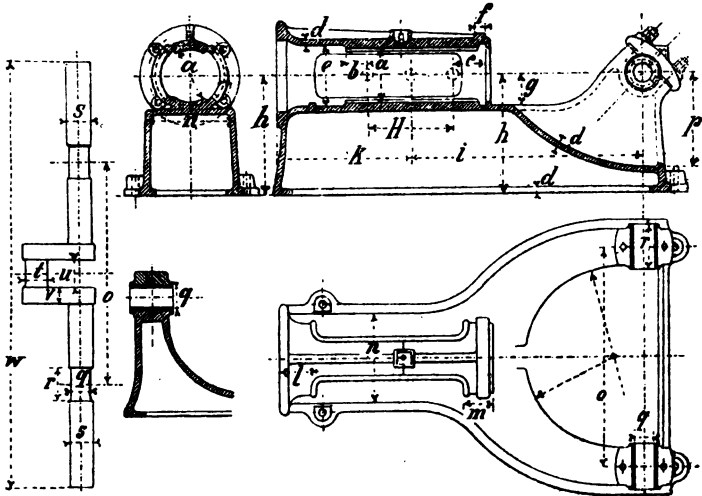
Dampfmaschine mit gekröpfter Welle.
